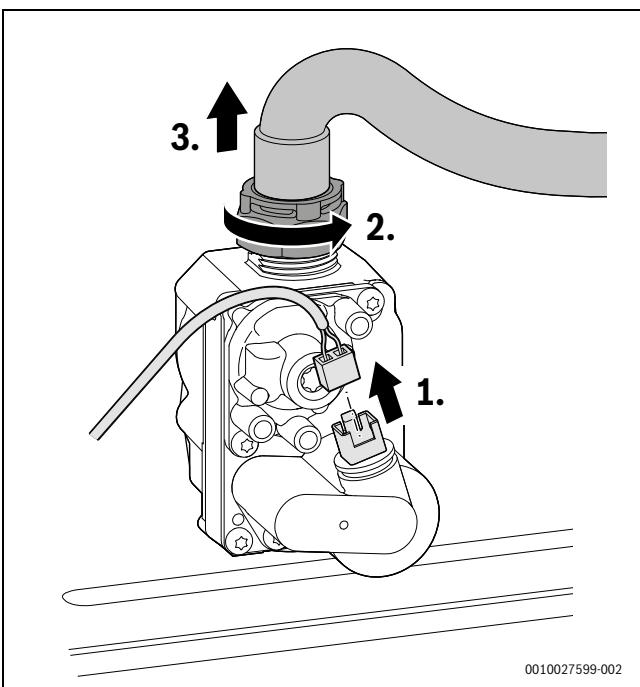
Stecker an der Gasarmatur abziehen und Überwurfmutter mit Gasschlauch abnehmen
